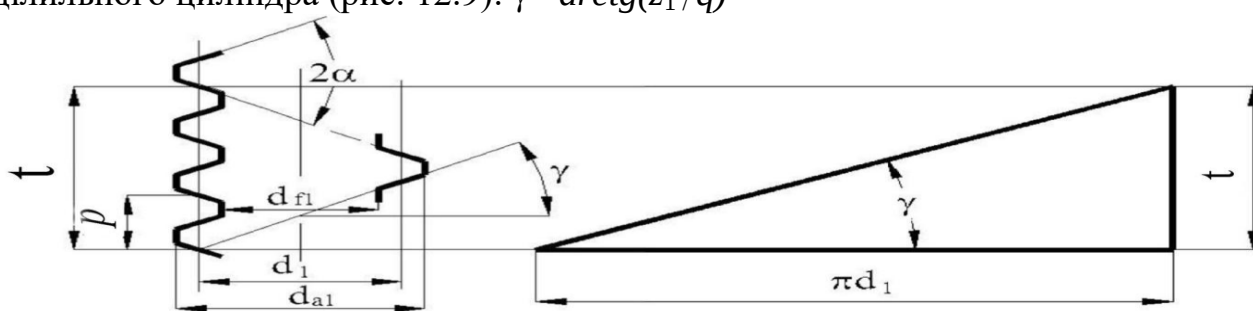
Розгортка дільного циліндра черв'яка
